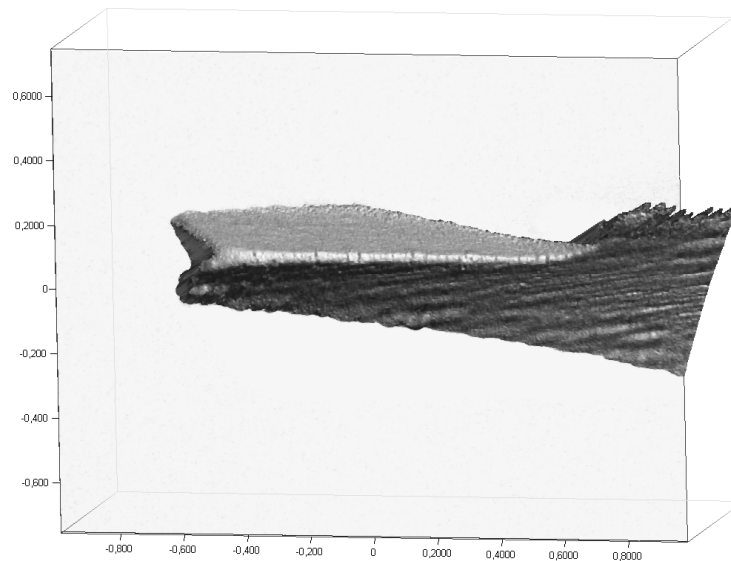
Schneidkante eines Gewindebohrers nach einer ca. 8 minütigen Bearbeitung in einer Schleppfinishmaschine der DF Serie
